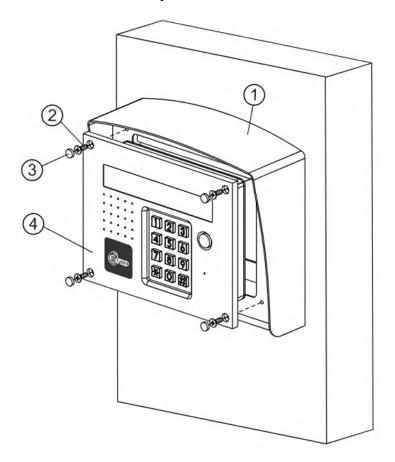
Установка блока вызова на наподвижной части металлической двери
